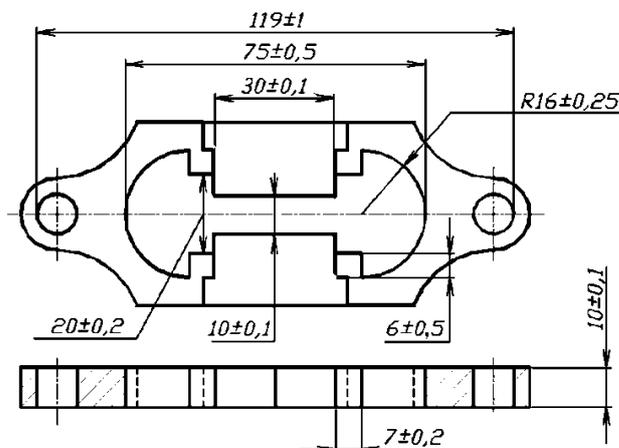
Основные размеры формы в сборе для ASTM D 6084
